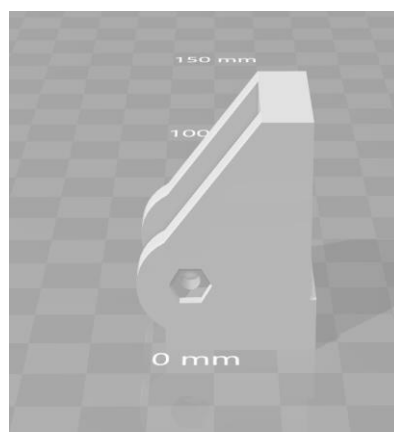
Držák motoru (2) – Autor: Rebel RepRap
